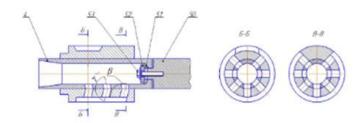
Устройство дросселя: 50 – балка направляющая; 51 – сферическая шайба; 52 – шайба, направляющая колесо; 53 – болт с разрезной шайбой
